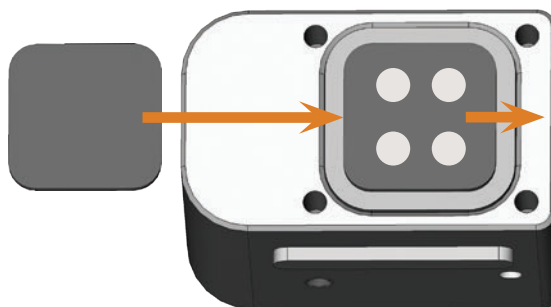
EL NUEVO INSERTO DEL ALMACÉN DE HERRAMIENTAS (IZQUIERDA, SIN TALADROS) SUSTITUYE AL INSERTO VIEJO (DERECHA, CON TALADROS)
